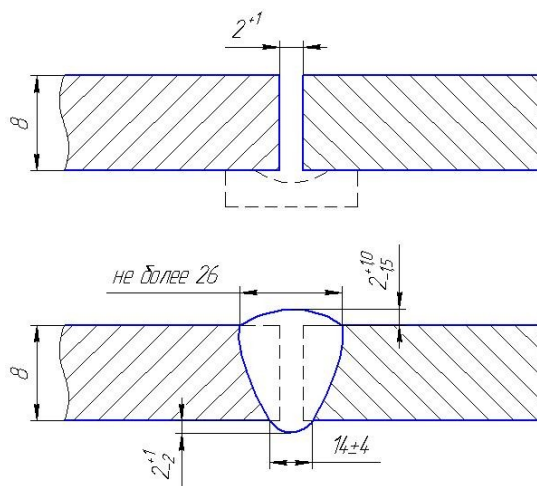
Сварное соединение для элементов опоры ВБР-25
